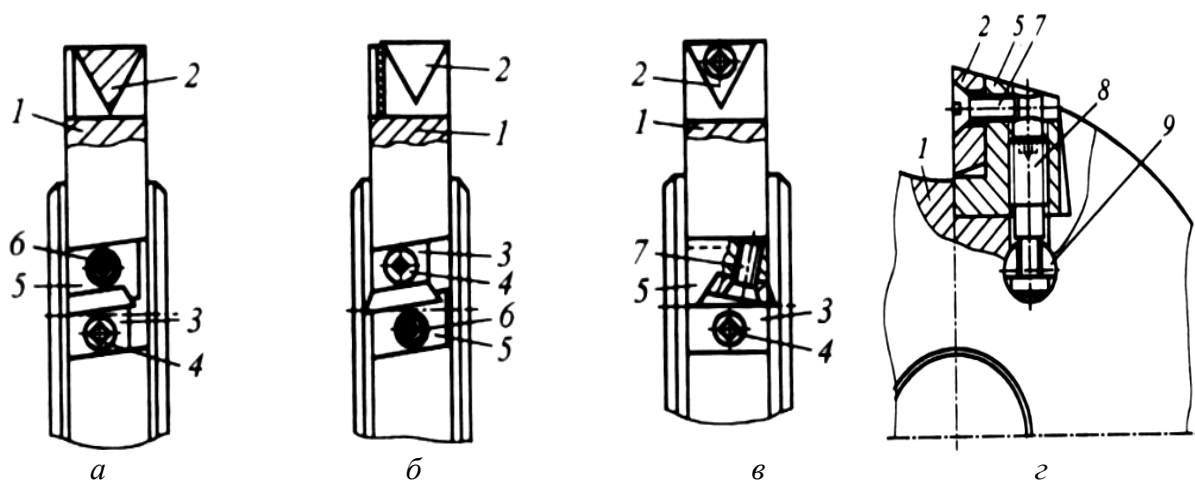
Основные конструкции сборных дисковых фрез с вкладышами для крепления СМП трехгранной формы
